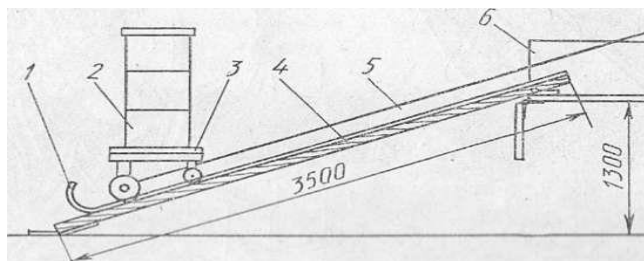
1 - упор; 2 — улей; 3 — тележка; 4—платформа с рельсами; 5 —тяга; 6 — кузов автомашины
